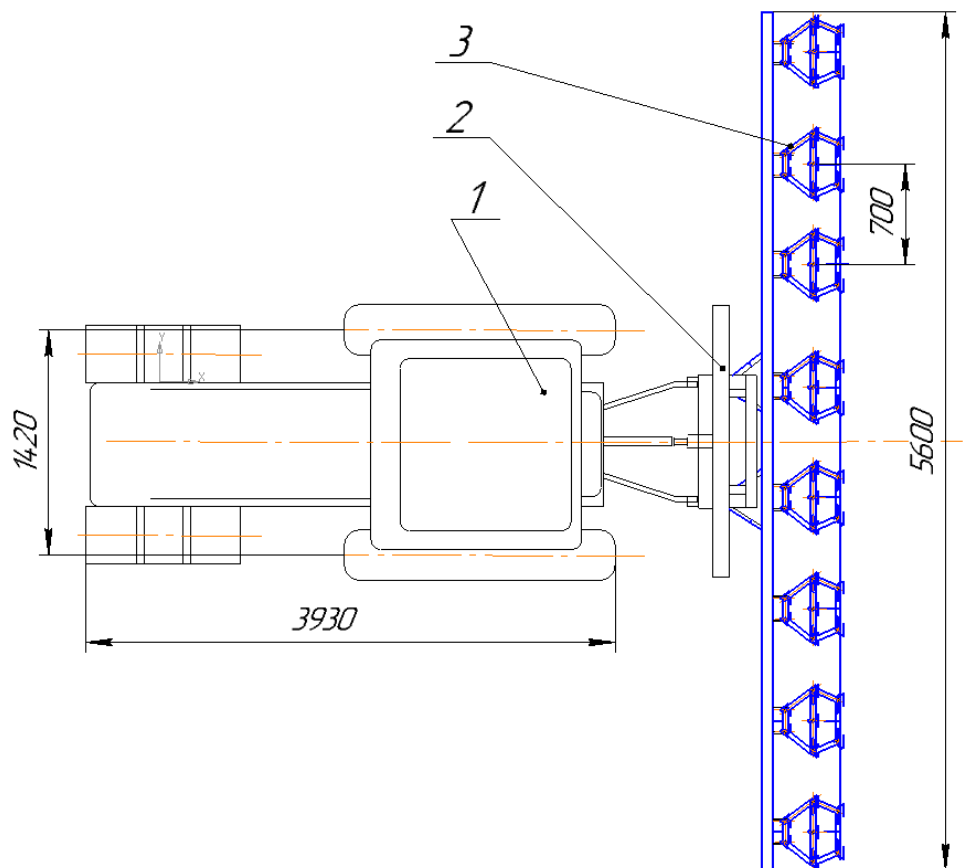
Схема агрегату: 1 – трактор; 2 – начіпний механізм, зняряддя для смугового обробітку
